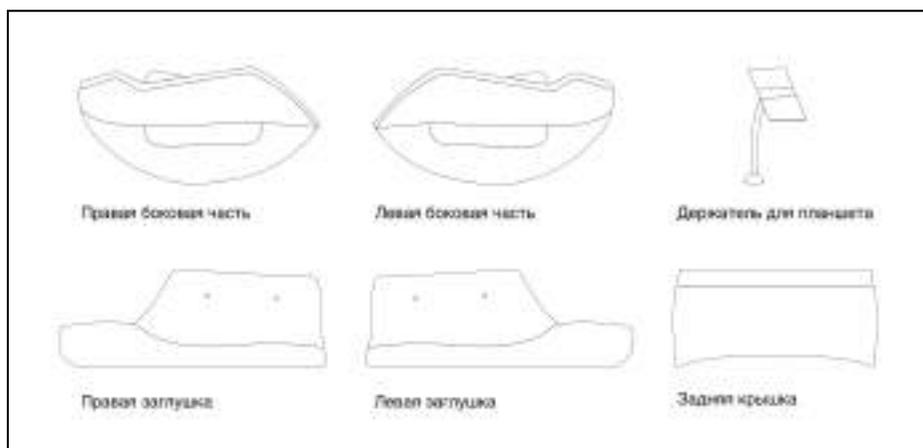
Левая и правая боковины массажного кресла, заглушки для нижней части корпуса, задняя крышка и держатель для планшета.
